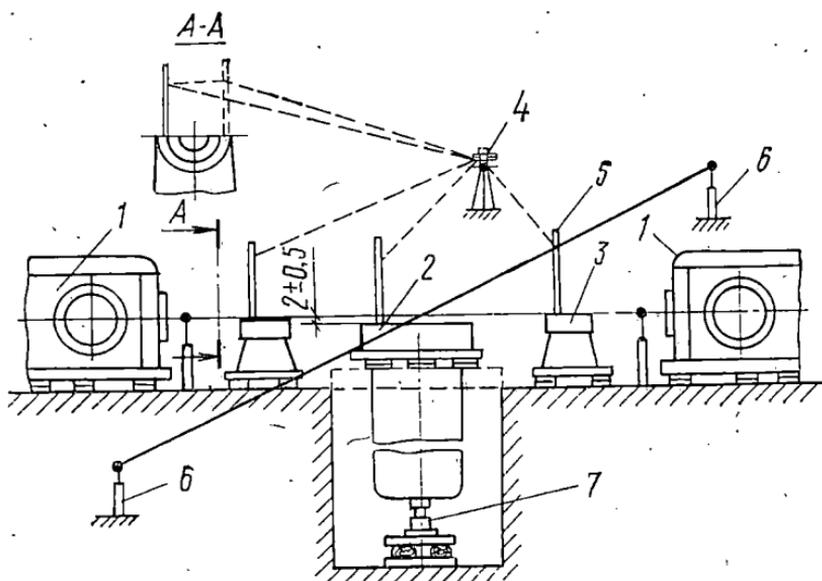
Схема монтажа электродвигателя двухкорпусного оппозитного компрессора
